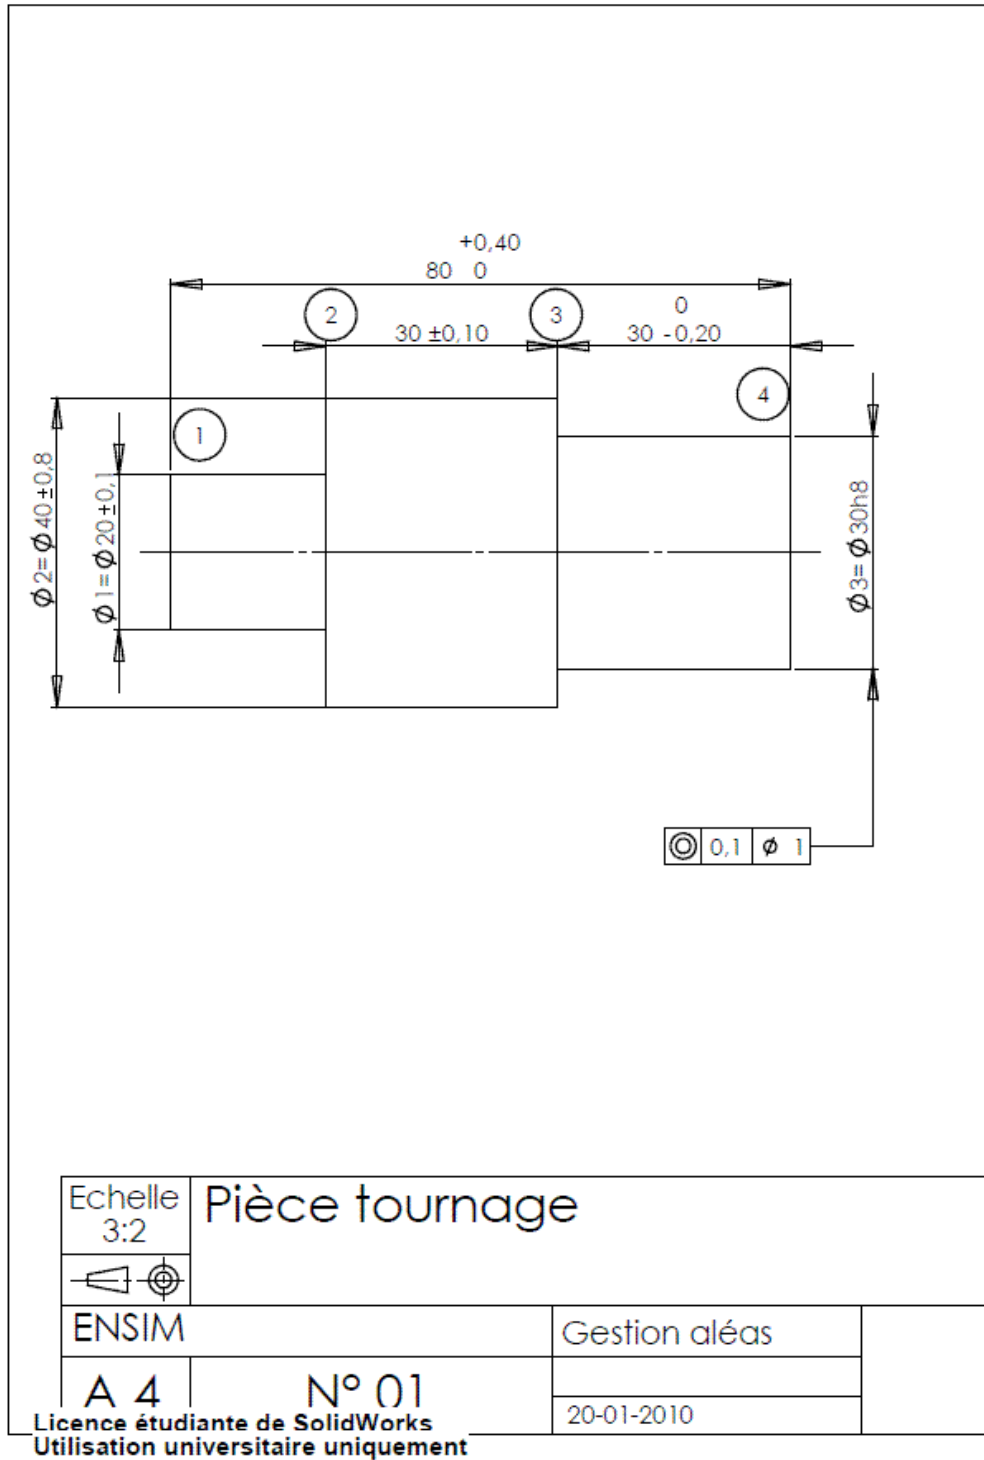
Dessin de définition d'une pièce à fabriquer.
